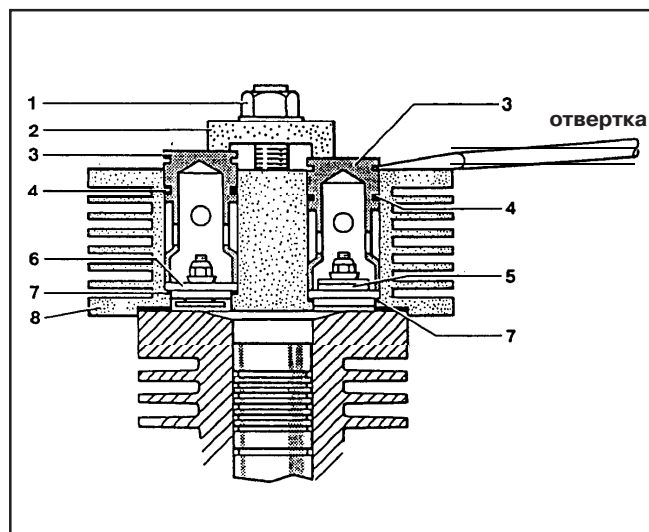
Головка клапана и клапаны, 2/3 ступень К180
